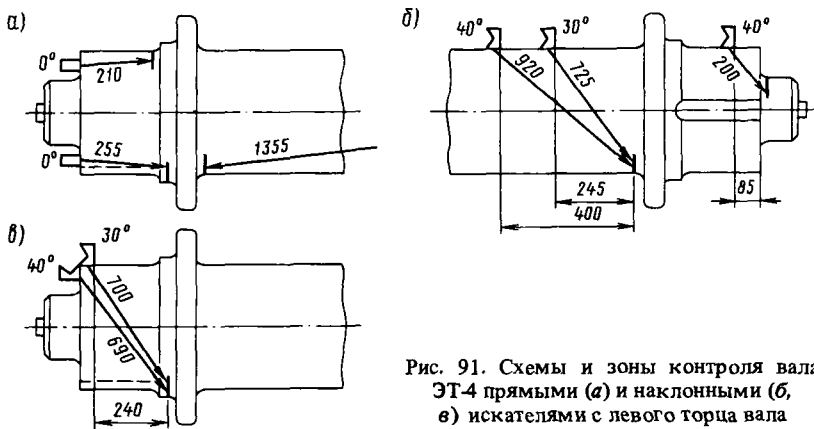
Схемы и зоны контроля вала ЭТ-4 прямыми (а) и наклонными (б, в) искателями с левого торца вала
